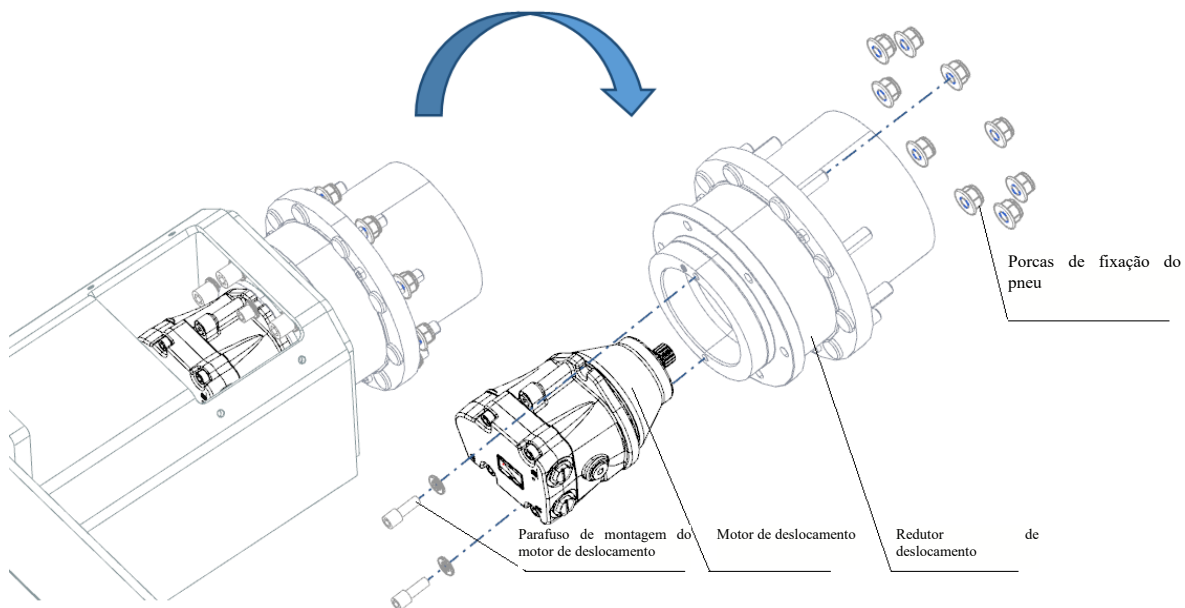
Diagrama de desmontagem do motor de deslocamento
